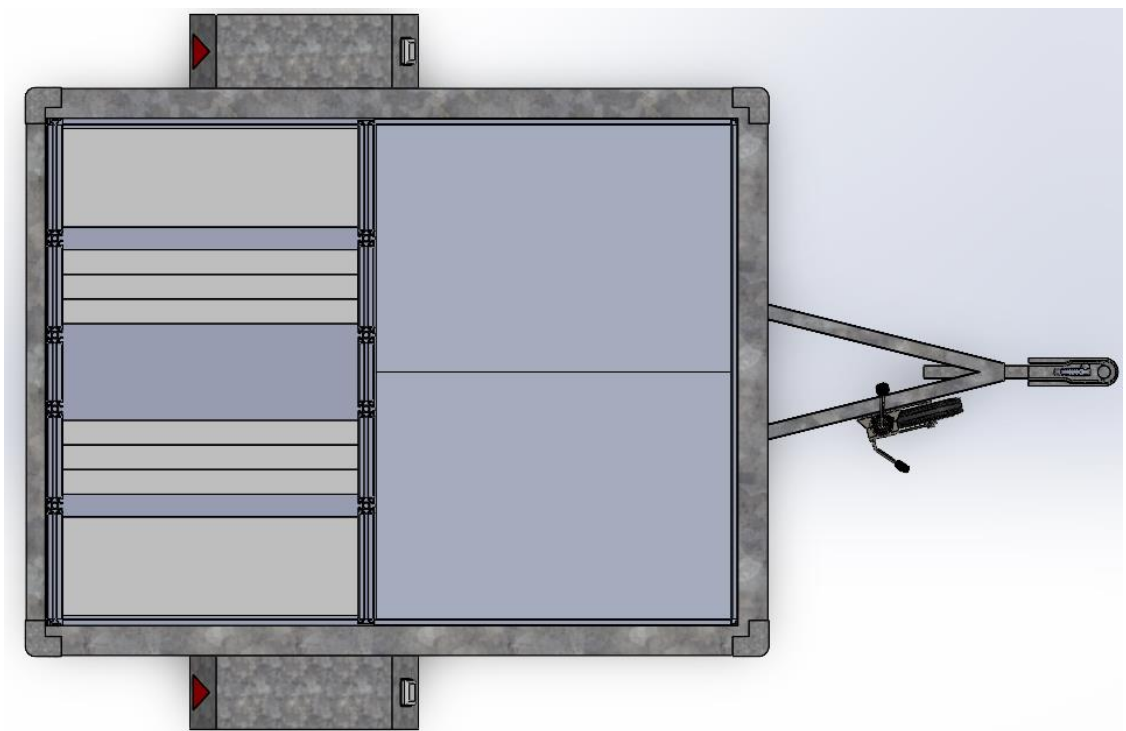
Vista planta (Fuente: Elaboración propia)
